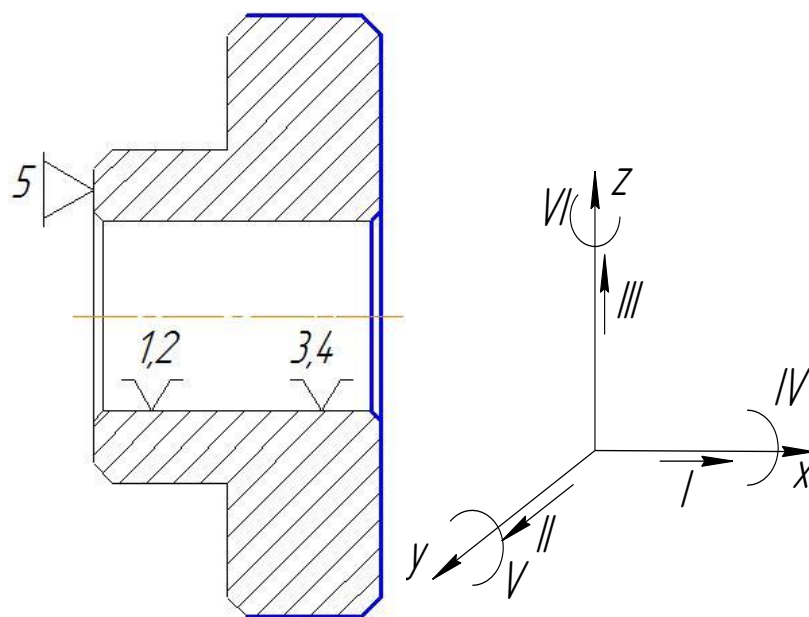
Схема базування заготовки на токарно-багаторіздевій операції
